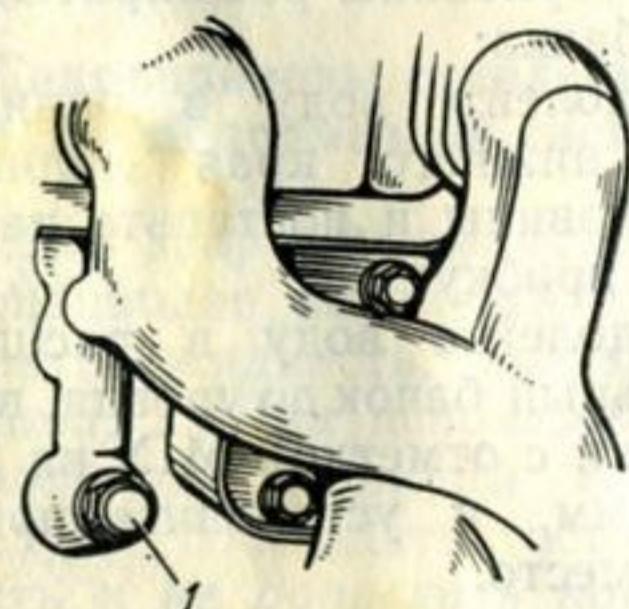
Пробка сливного отверстия на стенке рубашки блока цилиндров:
